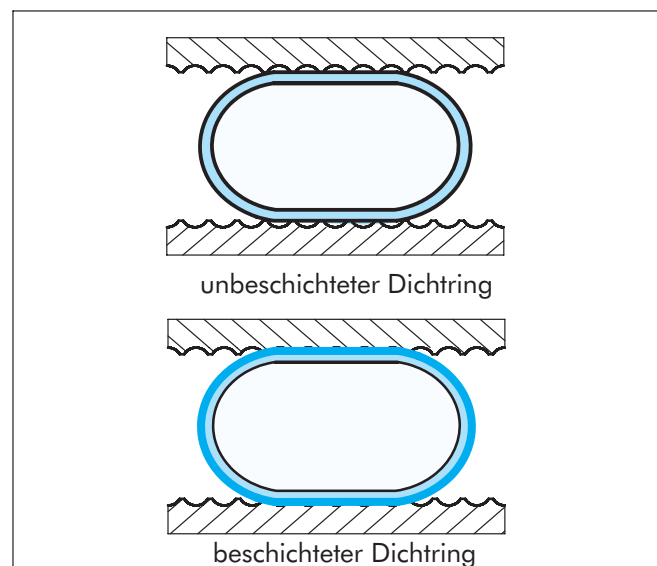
Kontaktfläche für beschichtete und unbeschichtete Wills Rings®
